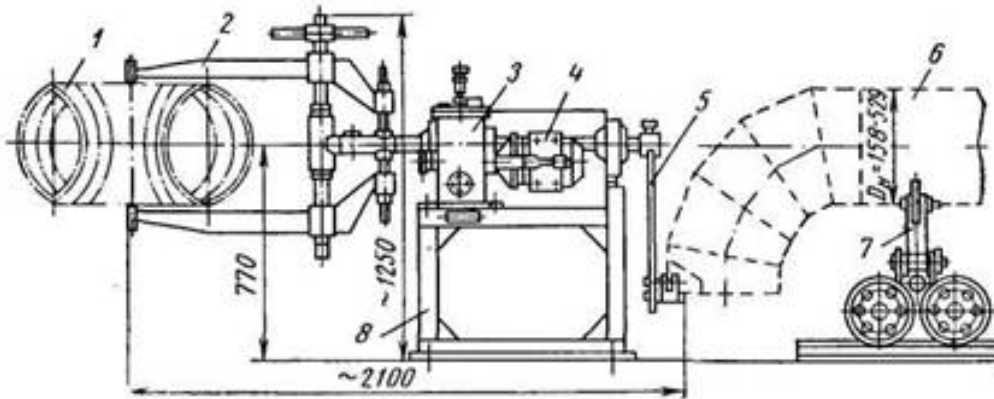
Установка для зварювання секційних відводів та приварювання їх до труб:
